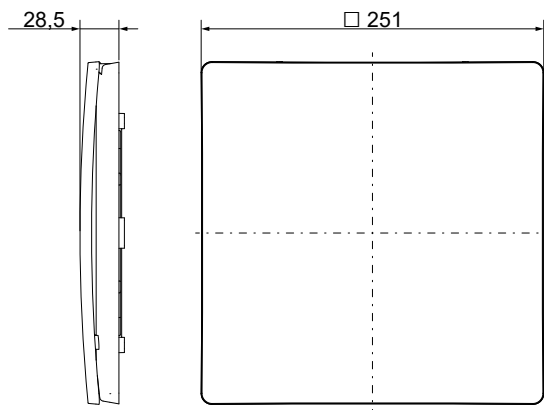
Maßzeichnung – Innenblende Abluftventilator Taxis
